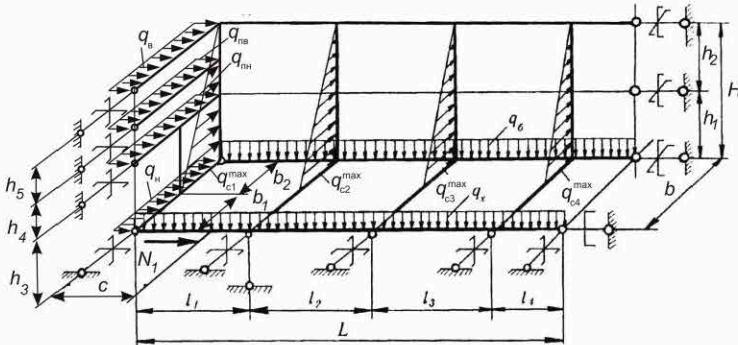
Расчетная схема 1/4 части кузова полувагона с глухими торцовыми стенами
